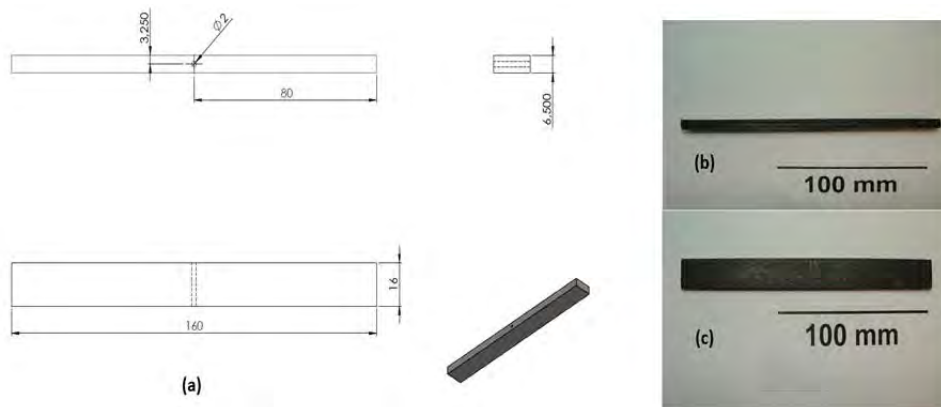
Corpo de Prova do tipo I. (a) Desenho com as dimensões do corpo de prova. (b) Vista Lateral. (c) Vista Frontal.
